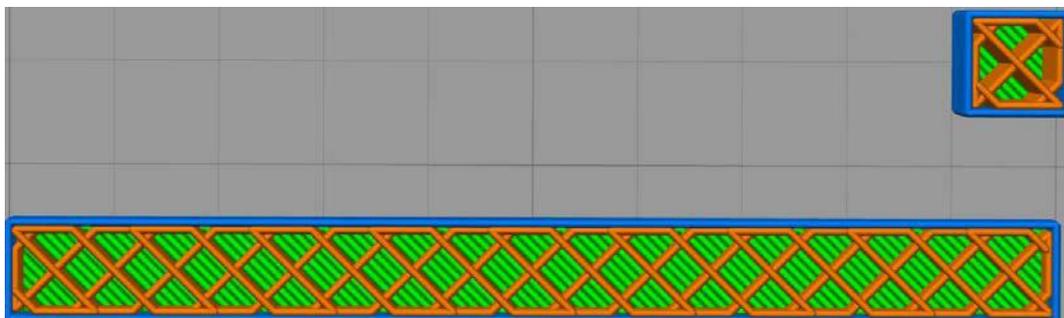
Objet pour essai destructif, imprimé à la verticale et à l'horizontale
